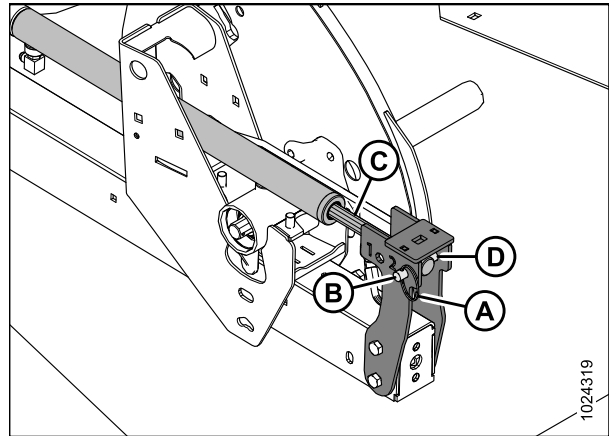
Цилиндр правого рычага мотовила в переднем положении
